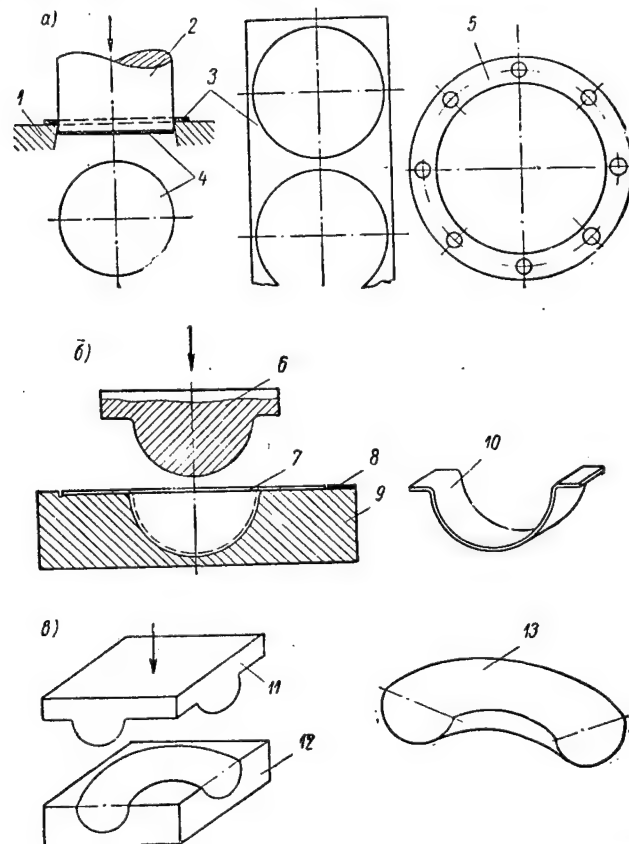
Виды штамповки: а — схема вырубki; б — схема гибки; в — схема вытяжки.
